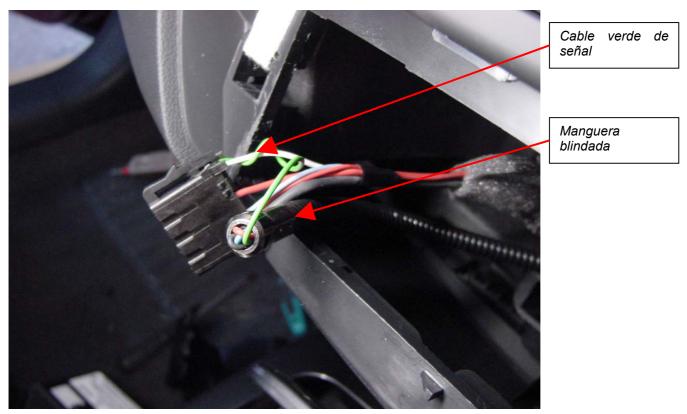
Vista del cable verde de señal soldado con la manguera blindada.
